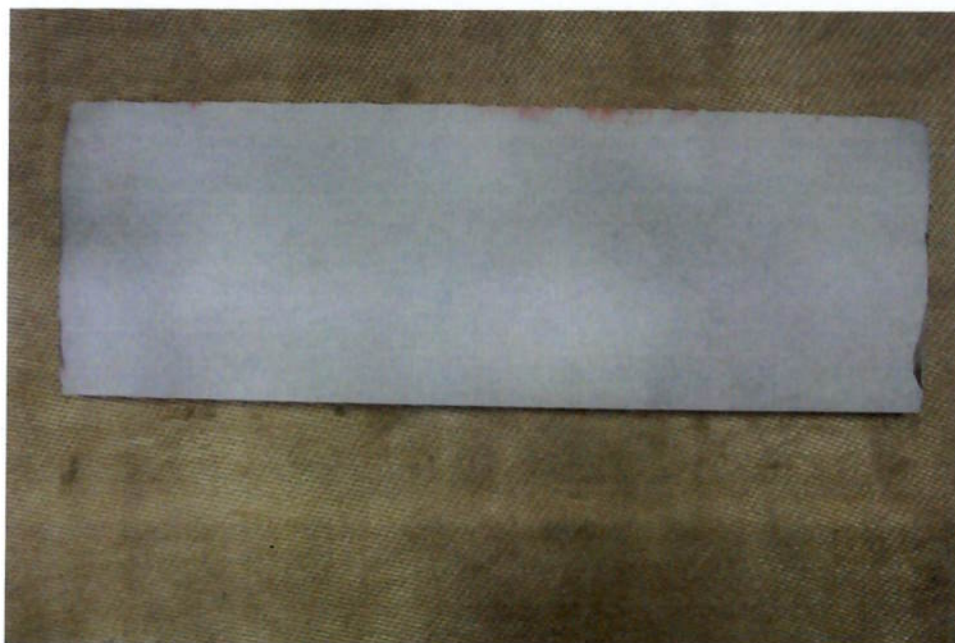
Corpo de Prova soldado com revelador, soldas sem defeitos
